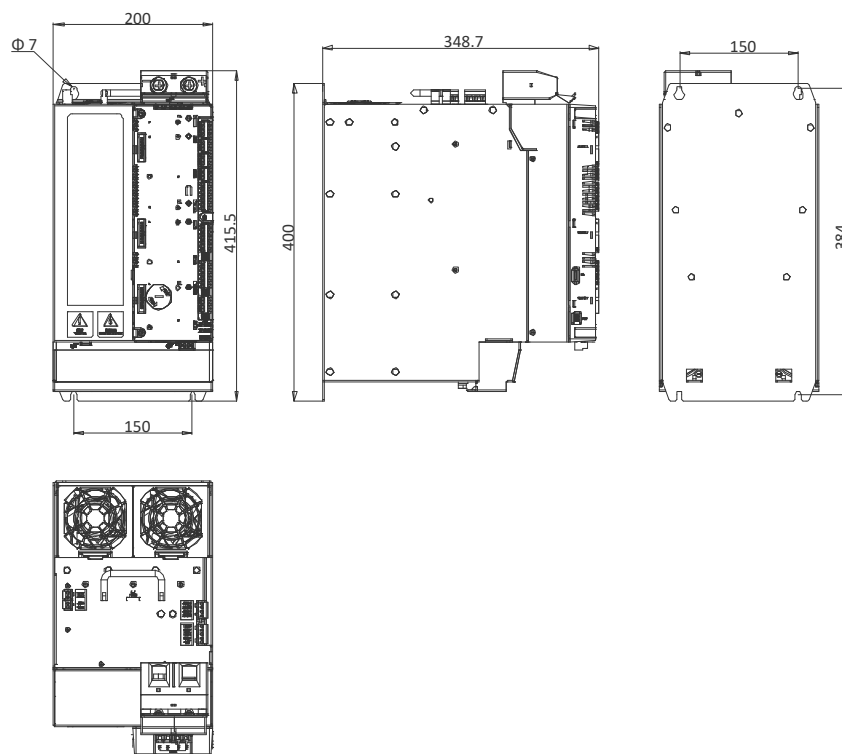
Габаритные размеры инвертора корпуса FR3 (мм)
